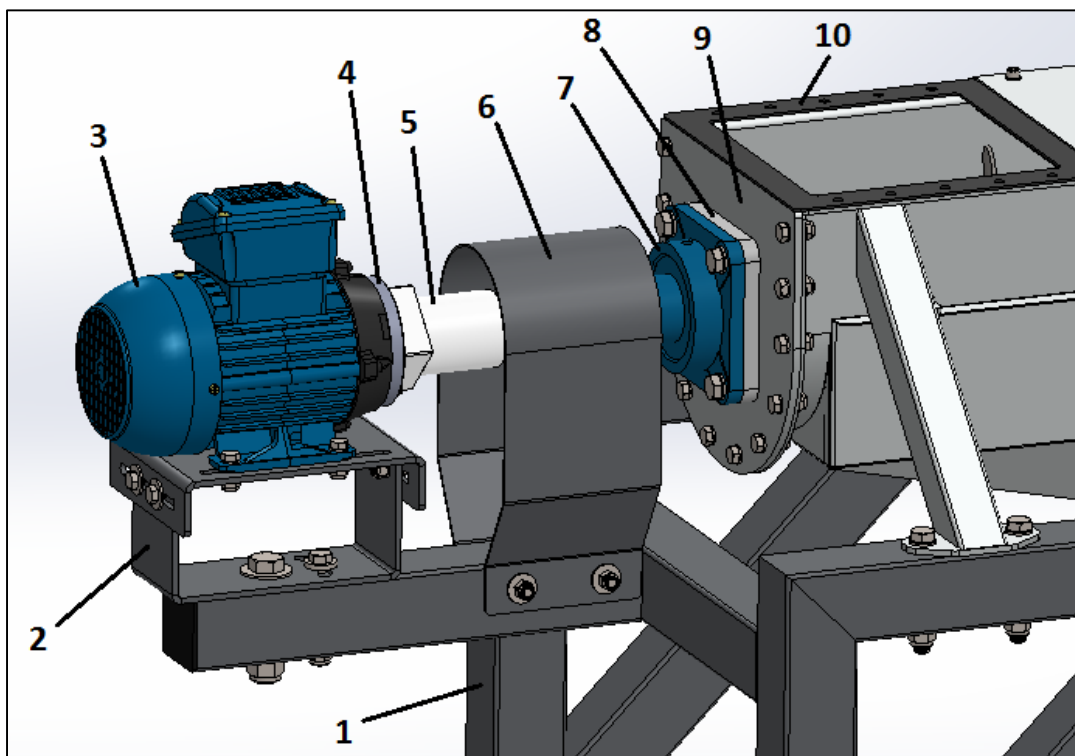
Vista ampliada de la conexión del sinfín con el motor. Referencia: 1) Carro. 2) Base regulable. 3) Motor trifásico. 4) Placa de adaptación. 5) Reductor planetario. 6) Protector. 7) Soporte de rodamiento axial. 8) Placa de alojamiento. 9) Tapa lateral. 10) Junta de caucho.
